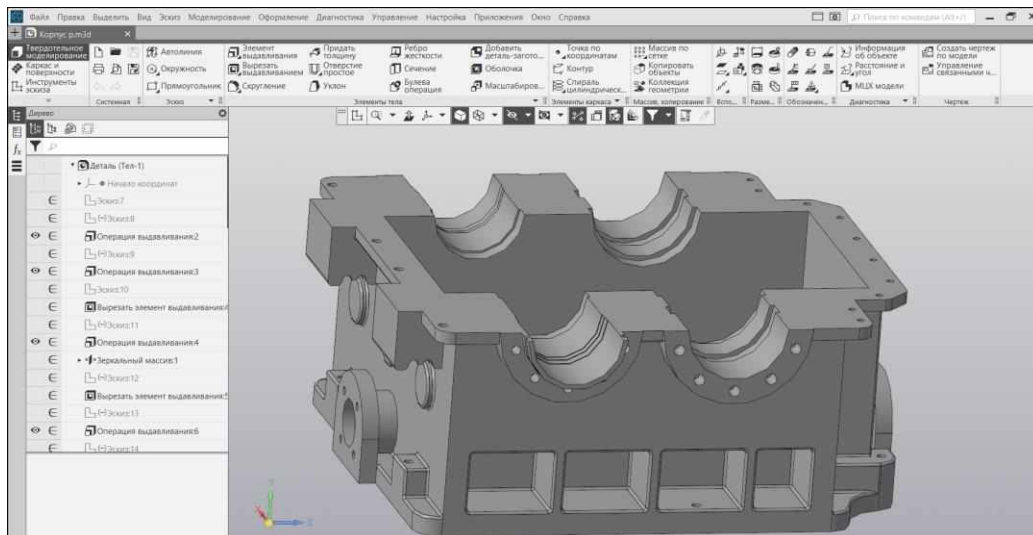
3D-модель корпусу редуктора побудована у середовищі САПР КОМПАС-3D
